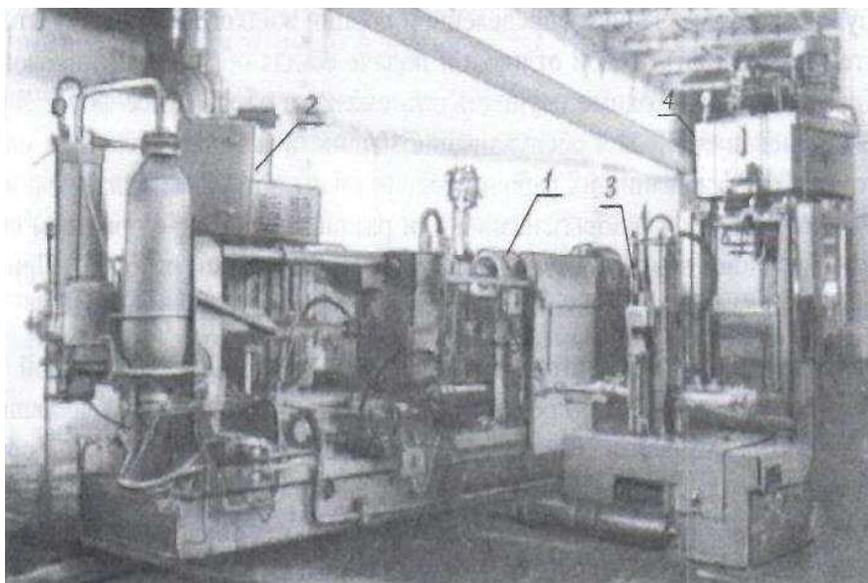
Роботизированный комплекс литья под давлением (вид со стороны робота, снимающего отливку) [4]:
